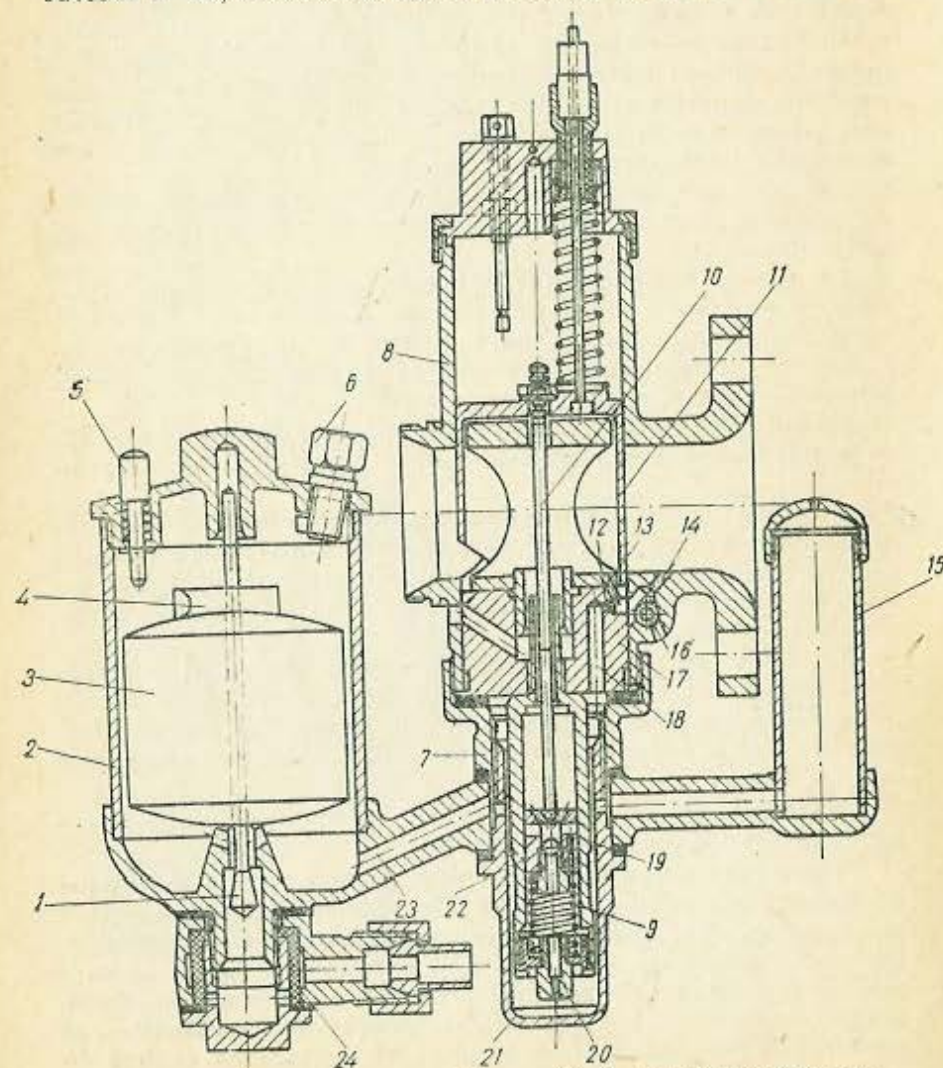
Carburatorul cu pompă de repriză și cameră de echilibrare.
